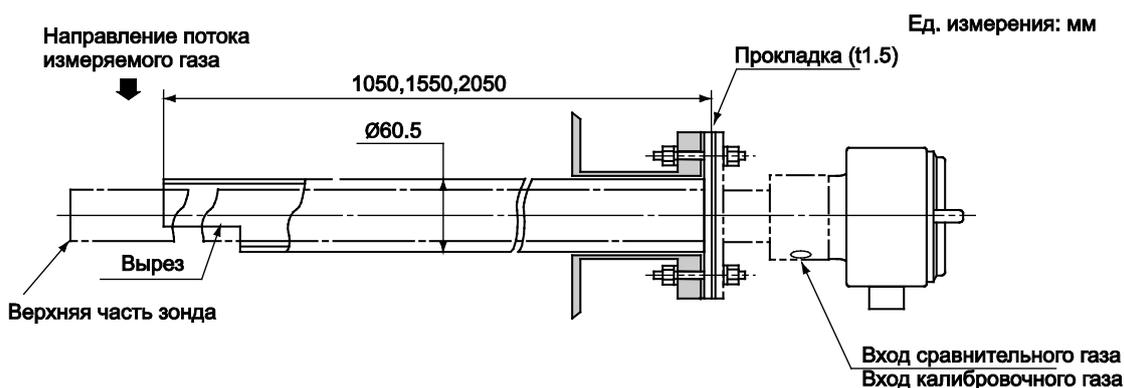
Защитное приспособление зонда (Усиливает монтажную прочность)
